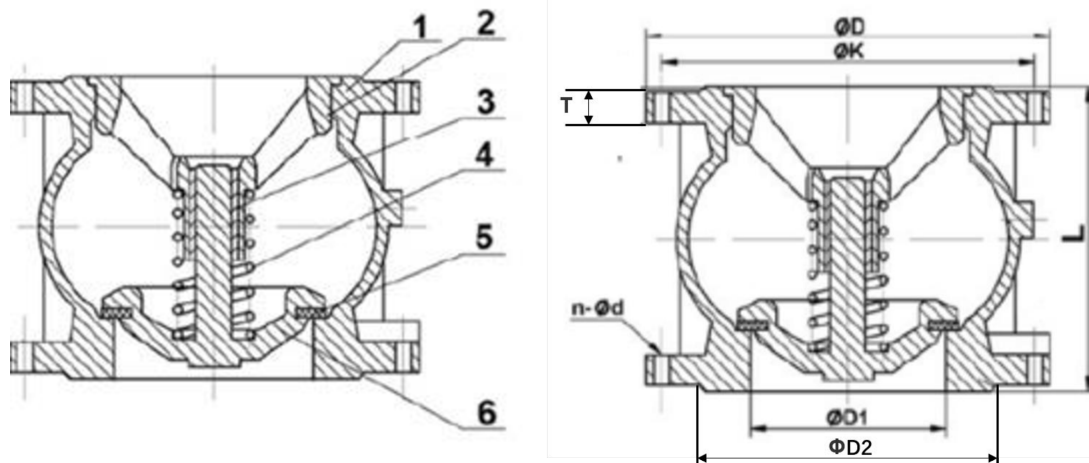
Клапан обратный чугунный пружинный фланцевый.
